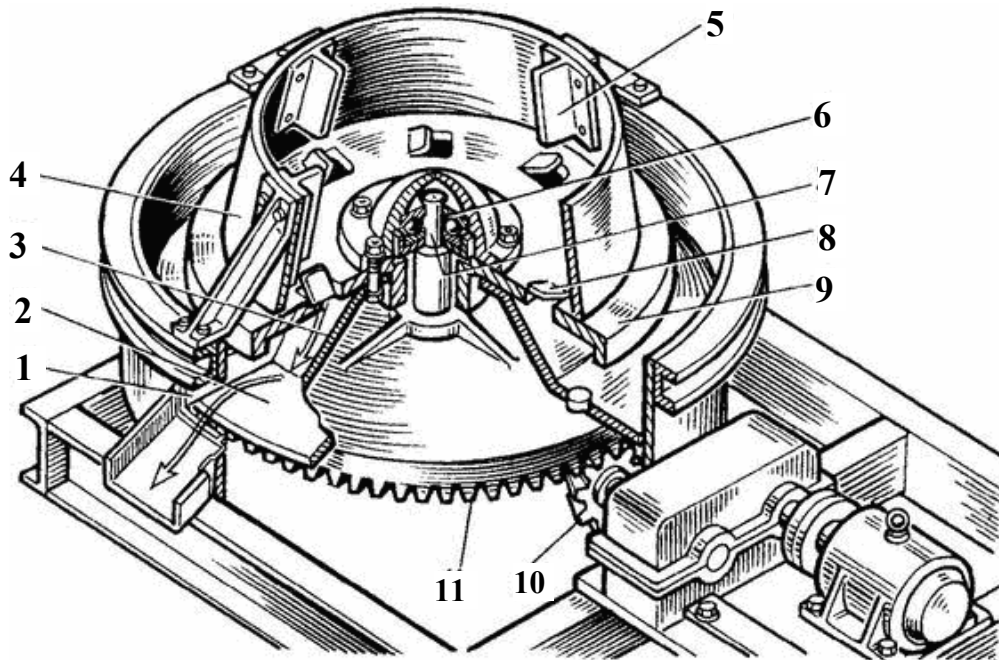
Лопатевий змішувач: 1 – скребок; 2 – тарілка; 3 – напрямний зрізаний конус; 4 – воронка; 5 – ребра; 6 – підп'ятник; 7 – вісь; 8 – ножі; 9 – диск; 10 – шестерня; 11 – кінчна шестерня
